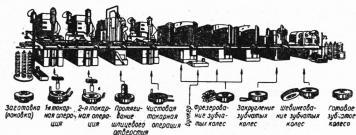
Автоматическая линия для изготовления зубчатых колес.
